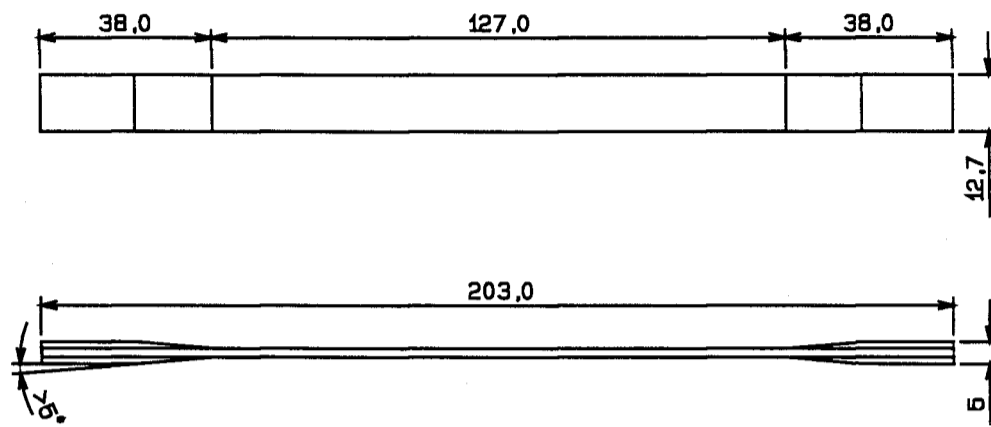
Geometria e dimensões do corpo-de-prova de tração longitudinal.
